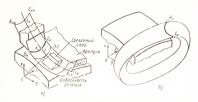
Поверхность резания, образуемая режущей кромкой инструмента
